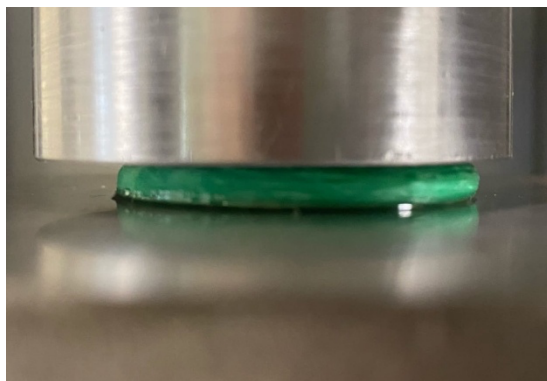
Цилиндрическая заготовка после процесса осадки
